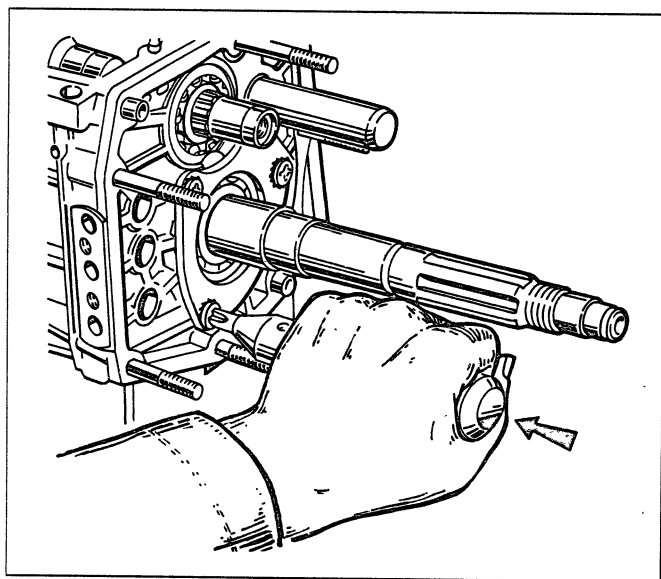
Извлечение промежуточного вала из картера коробки передач
